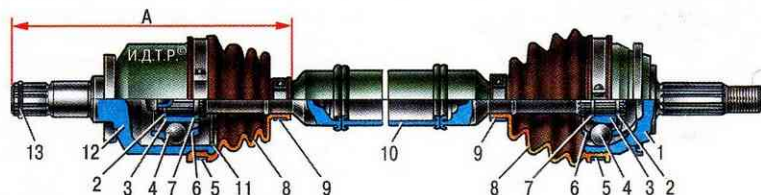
Привод передних колес: 1 – корпус наружного шарнира; 2 – стопорное кольцо; 3 – обойма; 4 – шарик; 5 – наружный хомут; 6 – сепаратор; 7 – упорное кольцо; 8 – защитный чехол; 9 – внутренний хомут; 10 – вал привода колеса; 11 – фиксатор внутреннего шарнира; 12 – корпус внутреннего шарнира; 13 – стопорное кольцо корпуса внутреннего шарнира; А – контрольный размер
